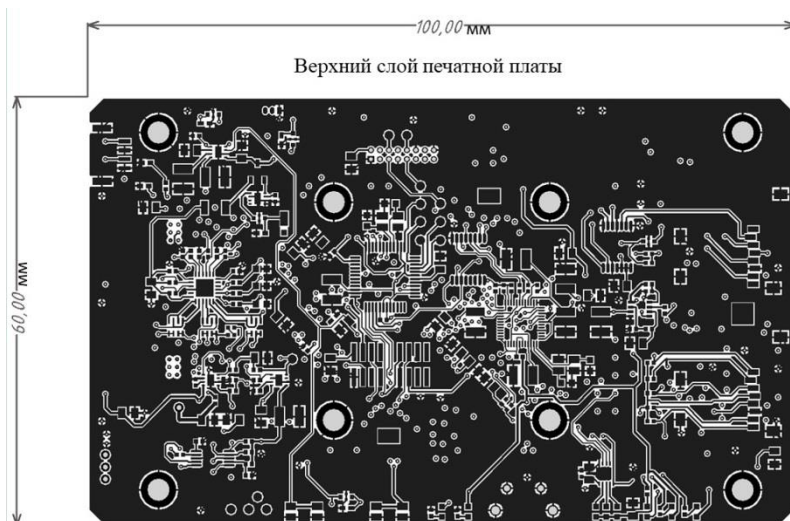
Верхний слой печатной платы полетного контроллера
